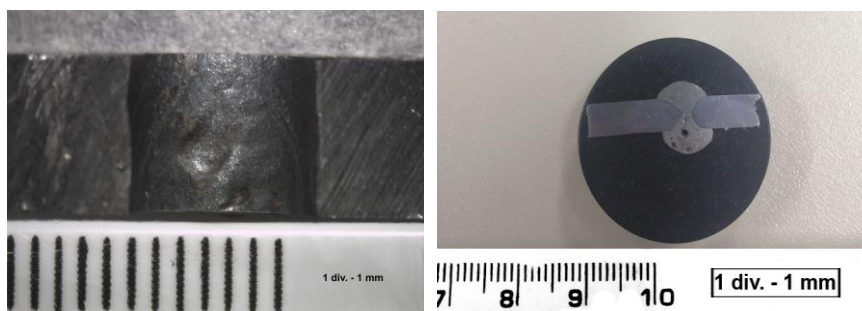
Detalhe superfície e perfil do cordão de solda do CP 1.
